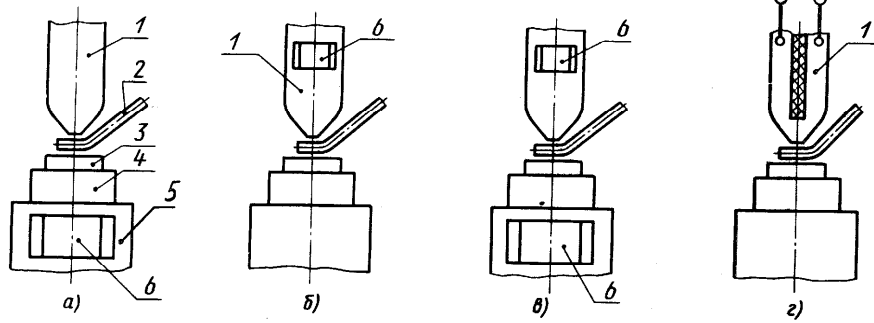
Варианты нагрева зоны соединения при термокомпрессионной сварке
